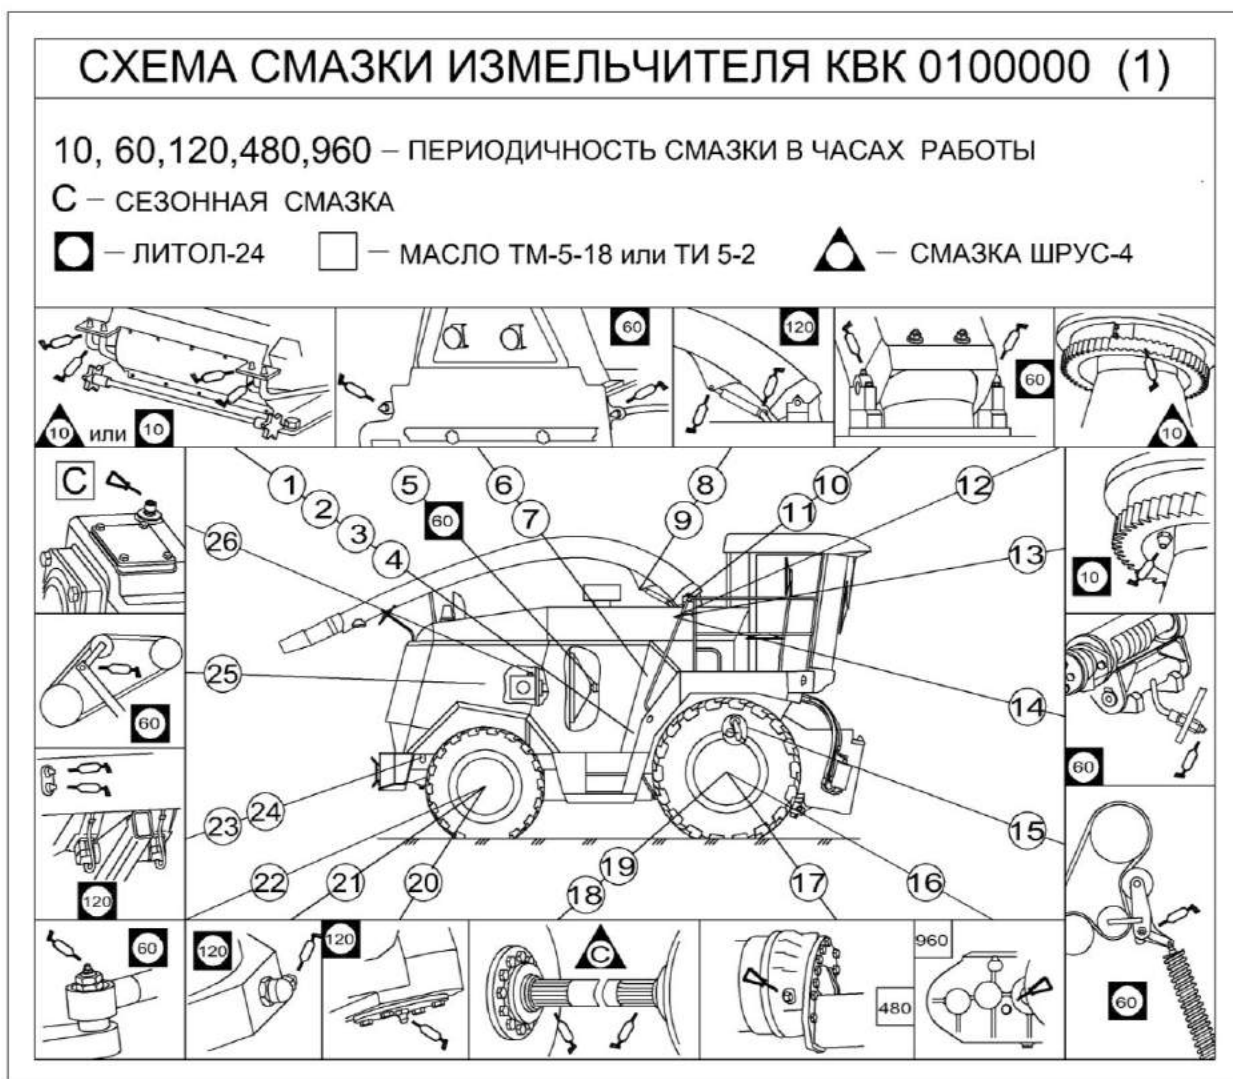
Схема смазки измельчителя КВК 0100000 (вид справа)
